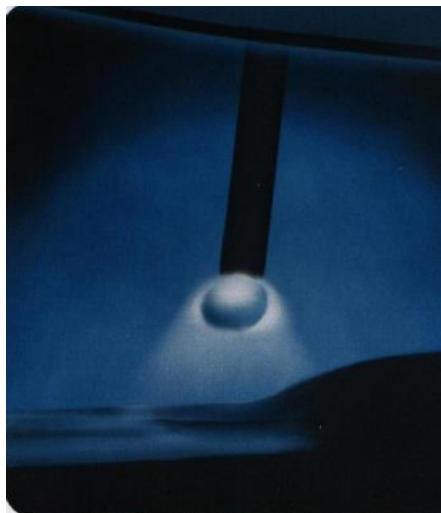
Koutový svar při metodě Control Weld[9]
